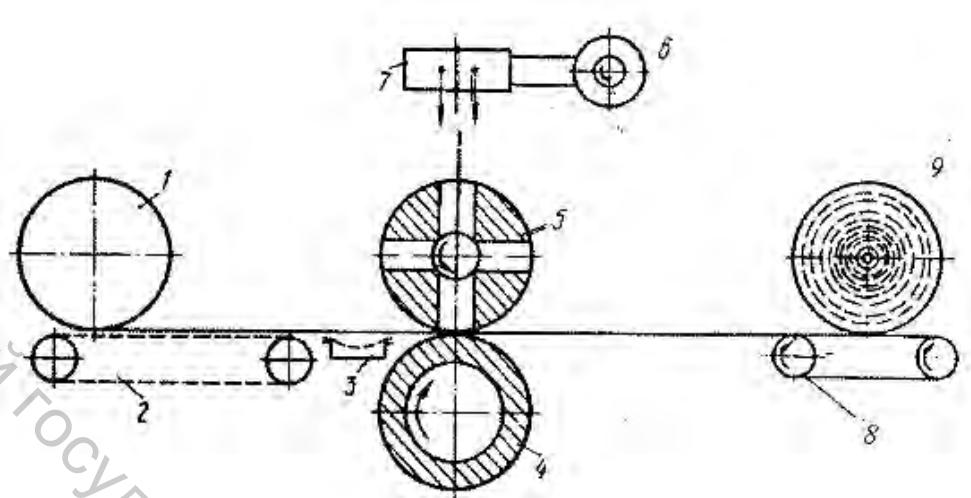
Схема установки для получения НМ точечной сваркой лучом лазера
